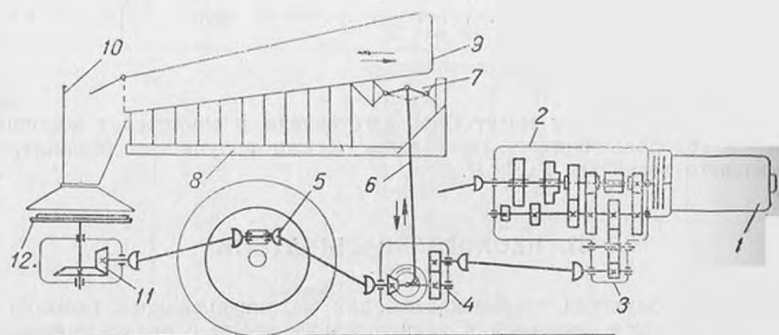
Кинематическая схема пескоразбрасывателя МПР-10:
